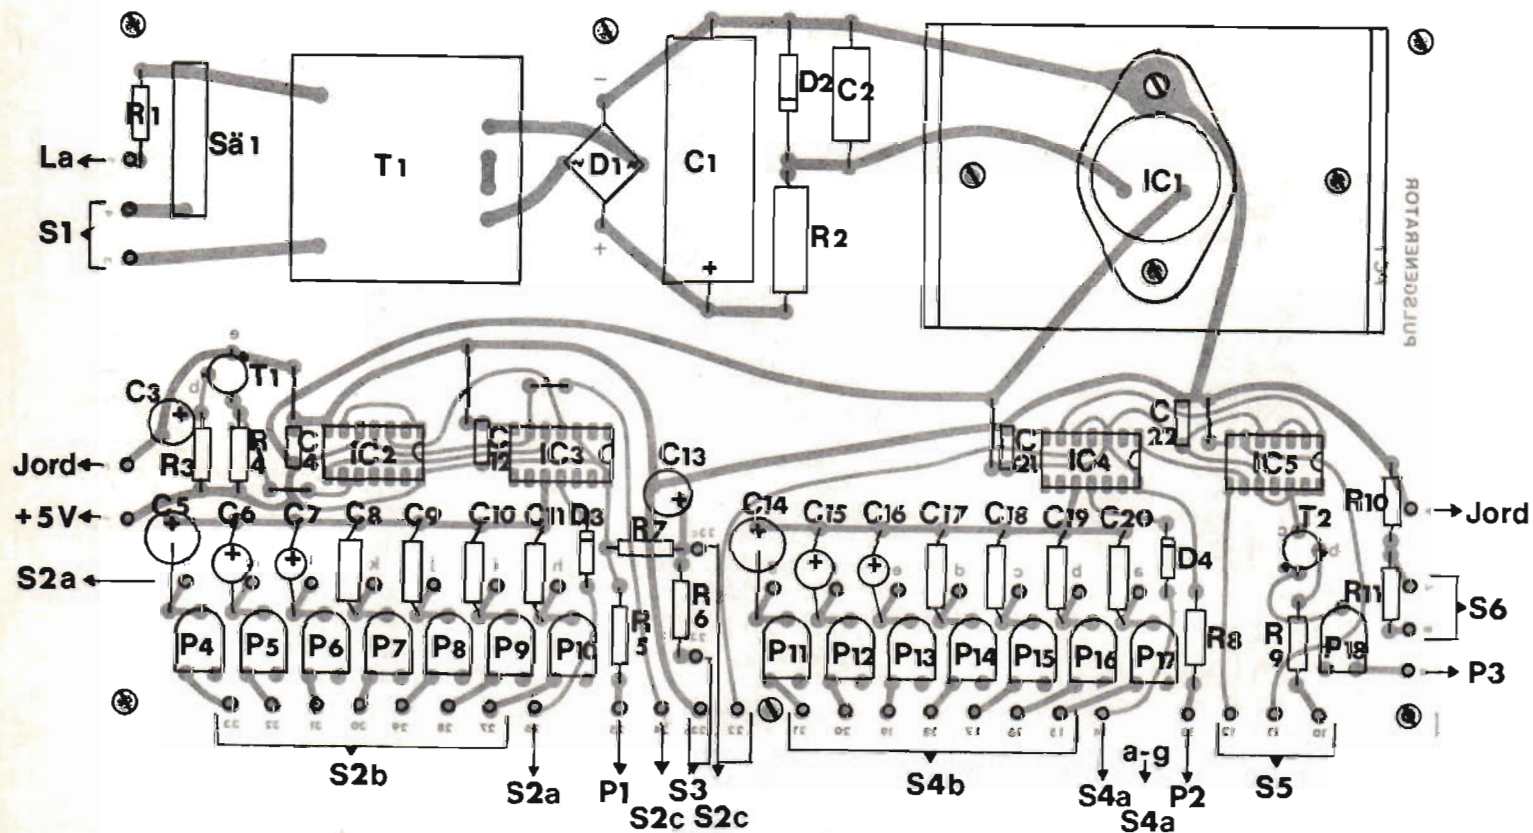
Komponenternas placering på kretskortet sett från komponentsidan.
